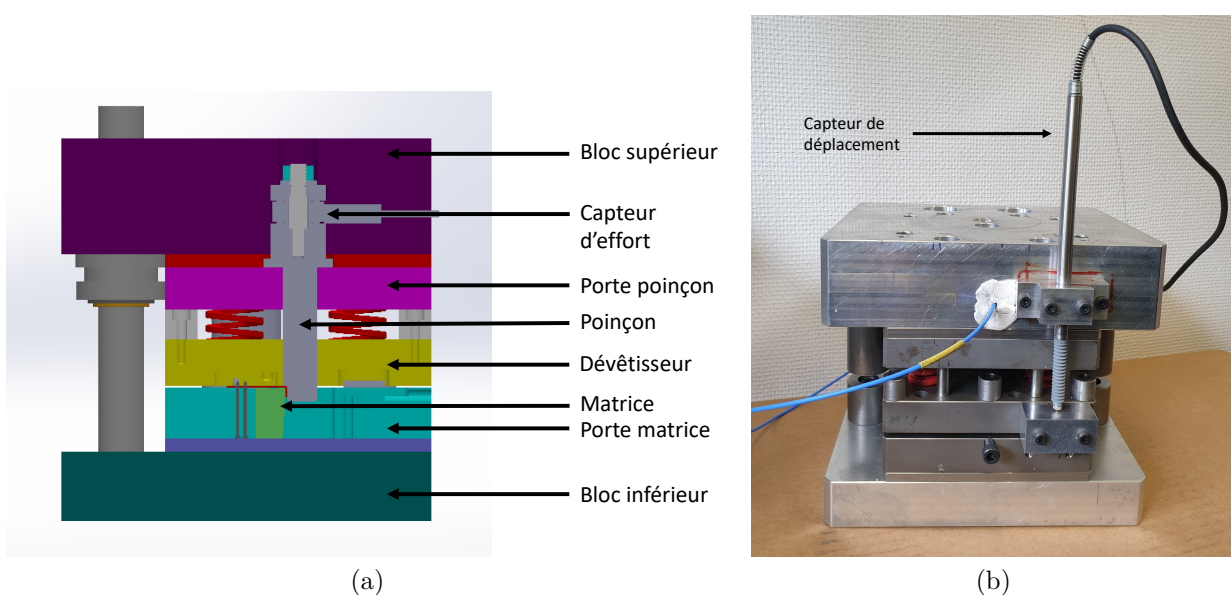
(a) Vue en coupe de l'outil de cambrage ; (b) Outil de cambrage
